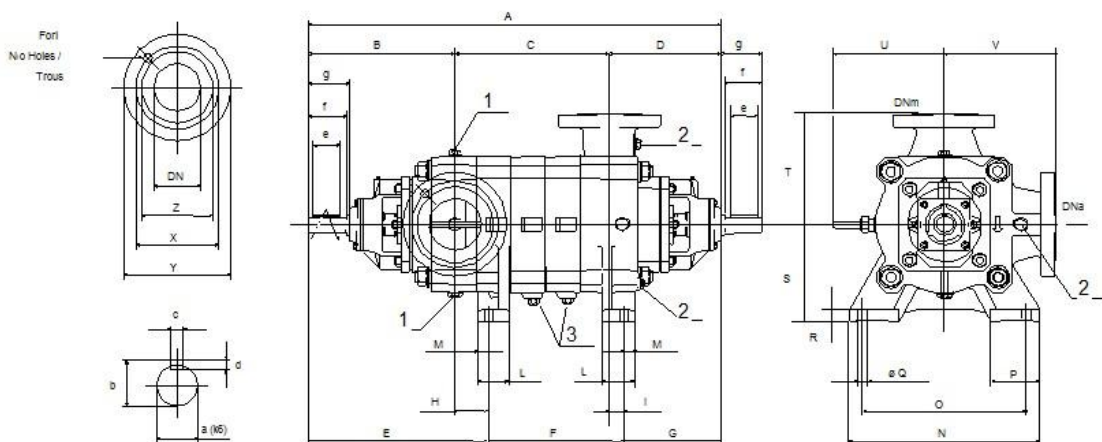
Dimensions de la pompe PM 100/ 2E
